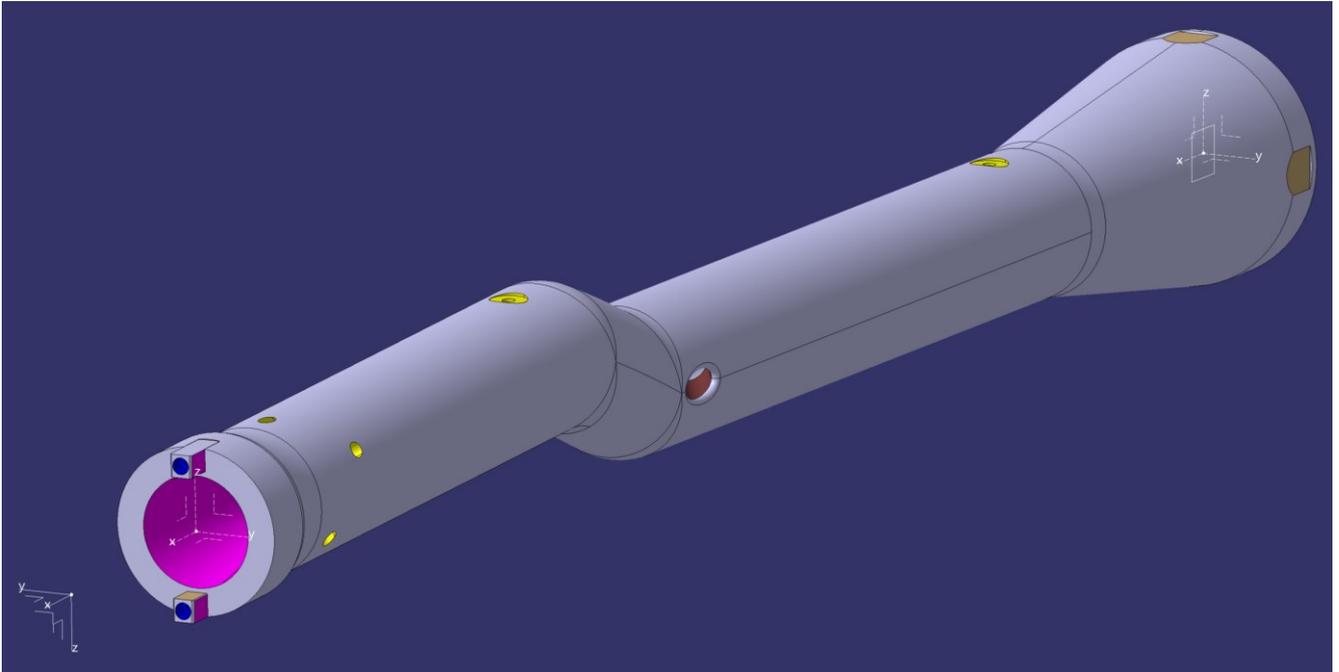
Vue d'ensemble des éléments à fabriquer (dard et clavettes)
